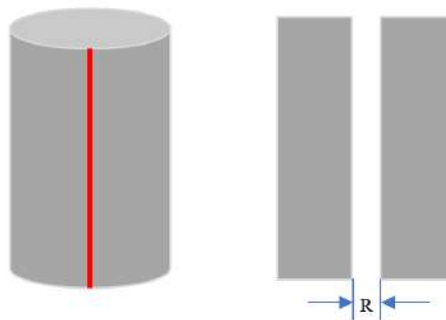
Representación de la soldadura en la sección cilíndrica.
